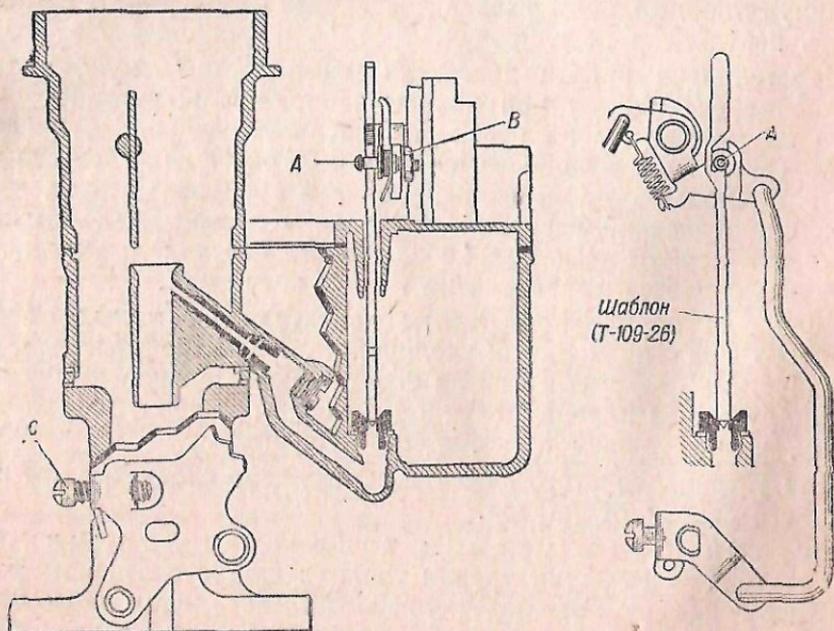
Проверка и регулировка положения калиброванной иглы главного дозирующего устройства
